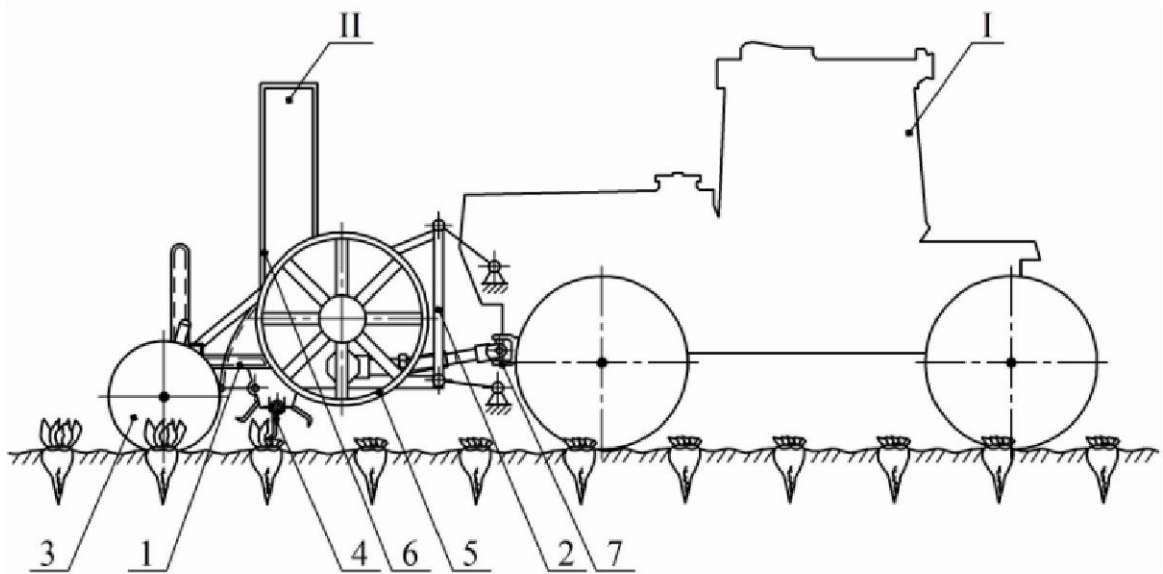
Конструкційна схема лабораторно-польової експериментальної установки: I – колісний орно-просапний трактор; II – фронтально начеплена гичкозбиральна машина; 1 – рама; 2 – начіпний пристрій; 3 – копіювальне колесо; 4 – роторний гичкозрізальний апарат; 5 – транспортувальний пристрій; 6 – завантажувальний пристрій; 7 – привод
